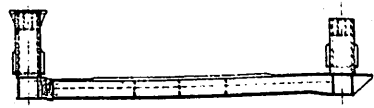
Tragrahmen für eine 180 PS dieselhydraulische Maschinenanlage für einen Aussichtstriebwagen, Motoren mit liegenden Zylindern.
